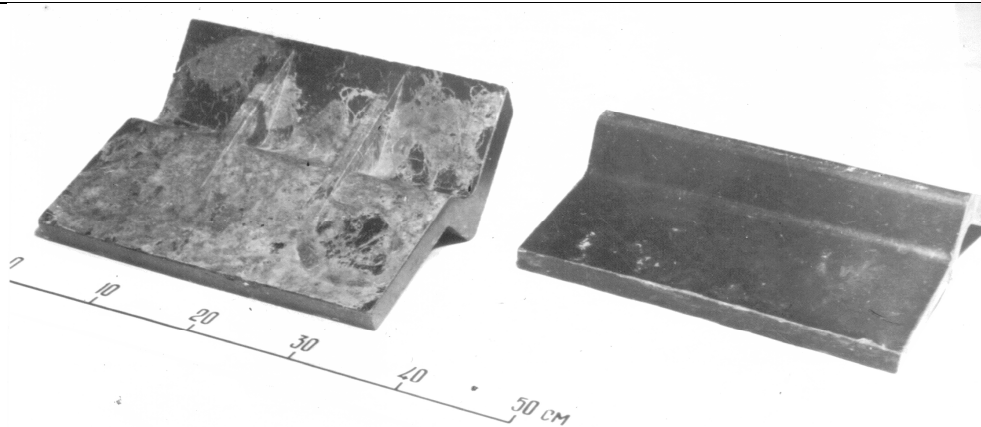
Ковши элеваторов шарошлифовальных станков МШ-33, изготовленные из армированного древопласта.
